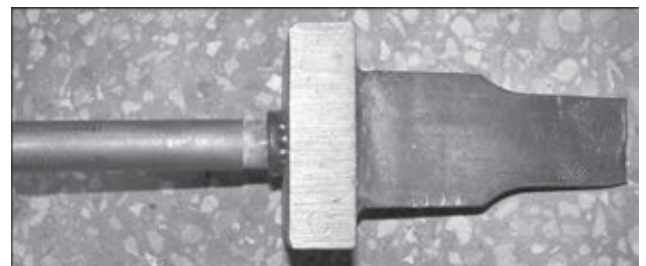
Общий вид сварного модельного образца для испытаний на усталость с призматической захватной частью
